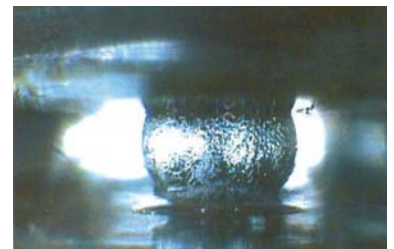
Дефект вторичного оплавления выводов микросхемы в корпусе BGA
